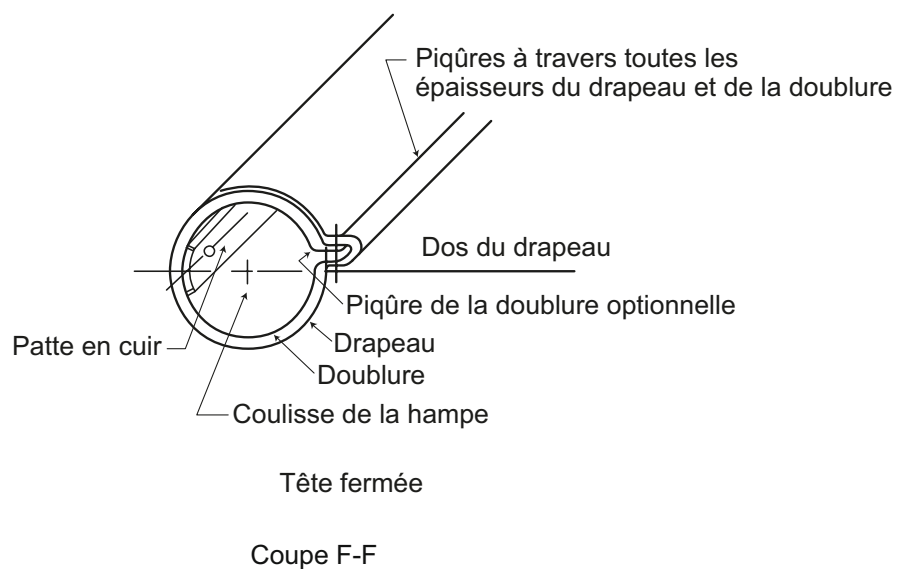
Détails de fabrication — Drapeau de sous-type 3A
